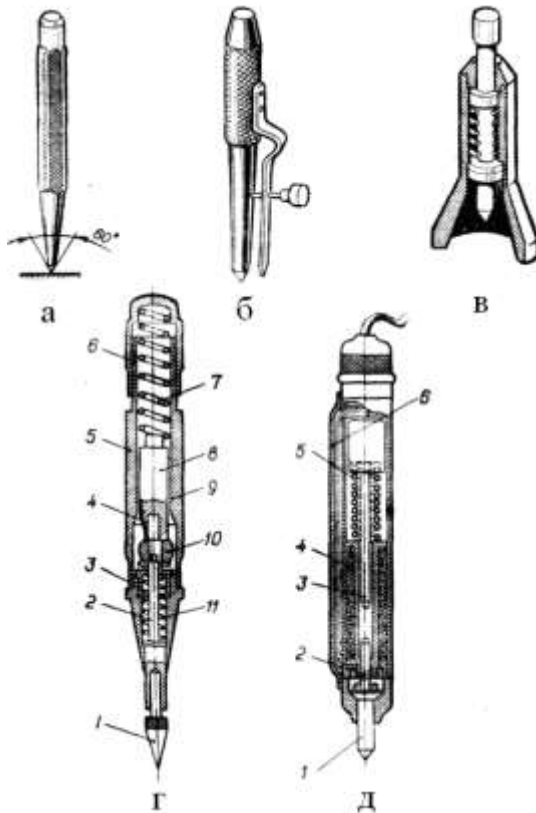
Кернери: а – звичайний; б – кернер-циркуль; в – кернер-дзвін (центрошукач); г – механічний (пружинний); електричний
